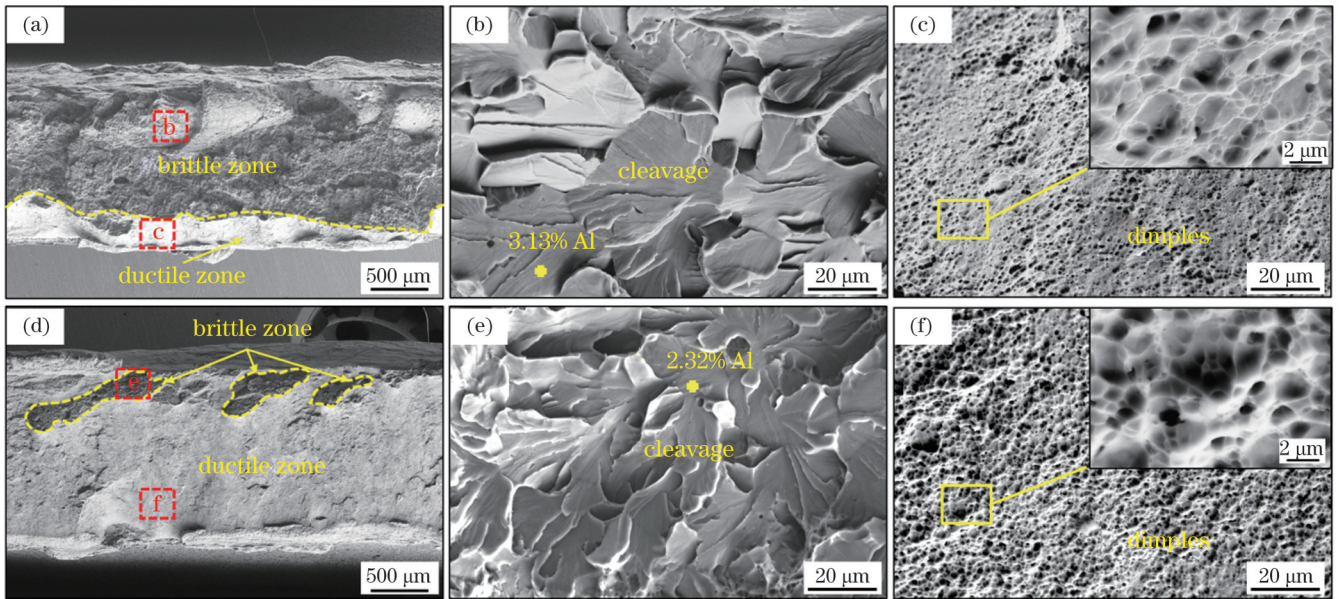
热冲压后焊接接头的断裂形貌。(a)~(c)LW 焊接接头;(d)~(f)OLFW2 焊接接头
